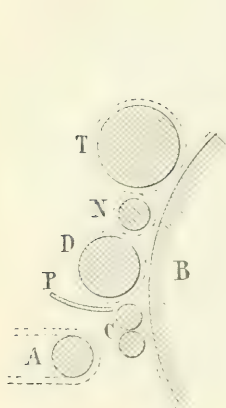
Schutzvorrichtung beim Entfernen des Flaumes.
